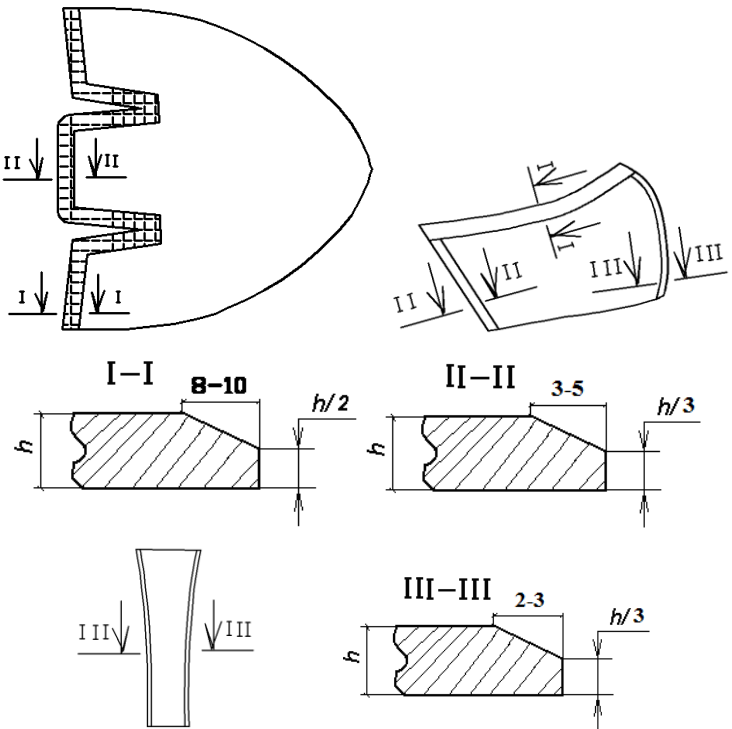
Схема складання заготовки жіночих літніх напівчеревику з бічними резинками
